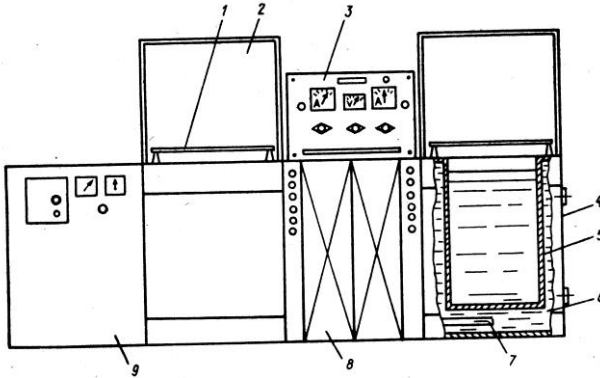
Установка для хромування деталей: 1 – штанги; 2 – кришка; 3 – пульт керування; 4 – корпус; 5 – внутрішня ванна; 6 – мінеральне масло; 7 – нагрівальний елемент; 8 – шафа з вентиляційною установкою; 9 – джерело живлення
